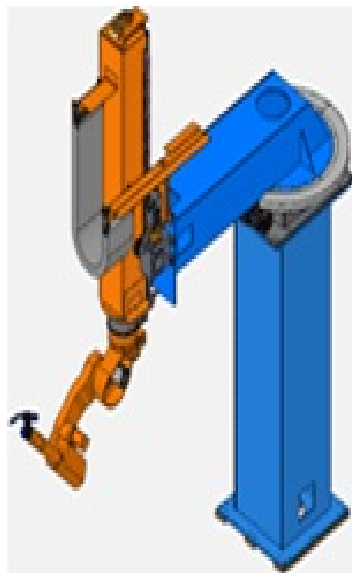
Сварочная колонна CSTD-V
